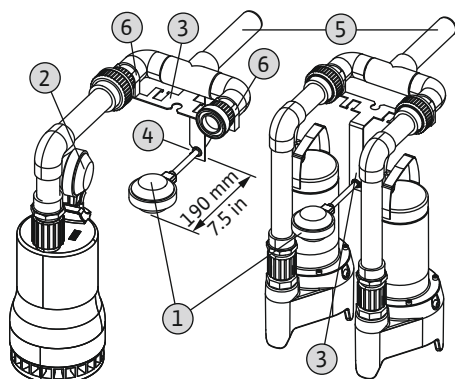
Крепление и настройка поплавкового выключателя, с прибором управления
